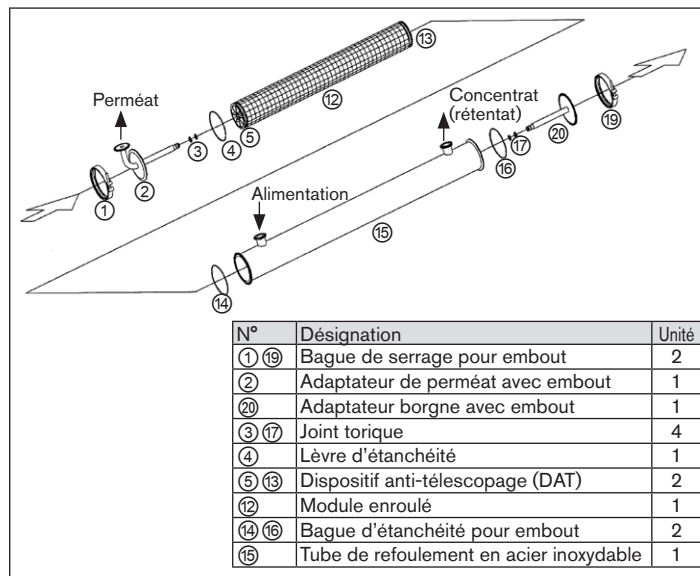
Montage d'un module unique dans le tube de refoulement
